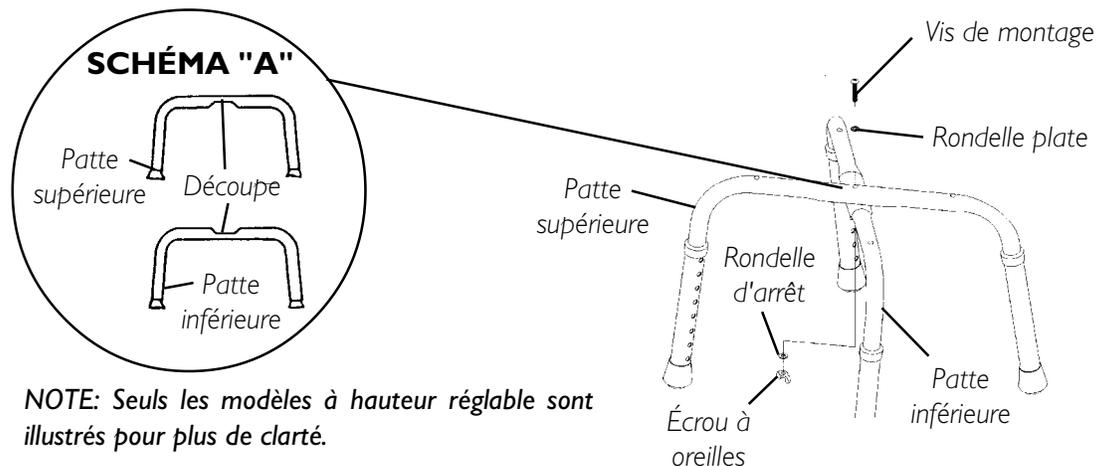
ASSEMBLER LE DOSSIER
